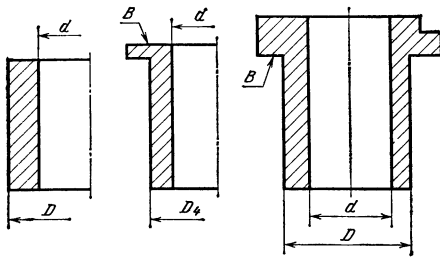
Схемы для определения допусков формы и расположения поверхностей кондукторных втулок
